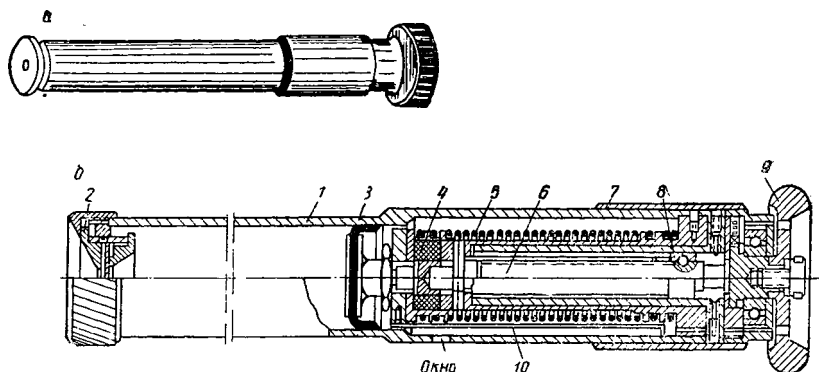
Счетчик пыли СН-2: а — общий вид; б — разрез
